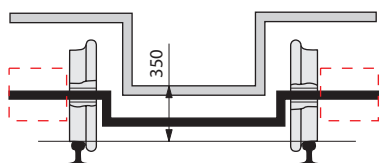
Ходовой механизм со свободно насаженными колесами и наружным расположением тягового и тормозного оборудования
